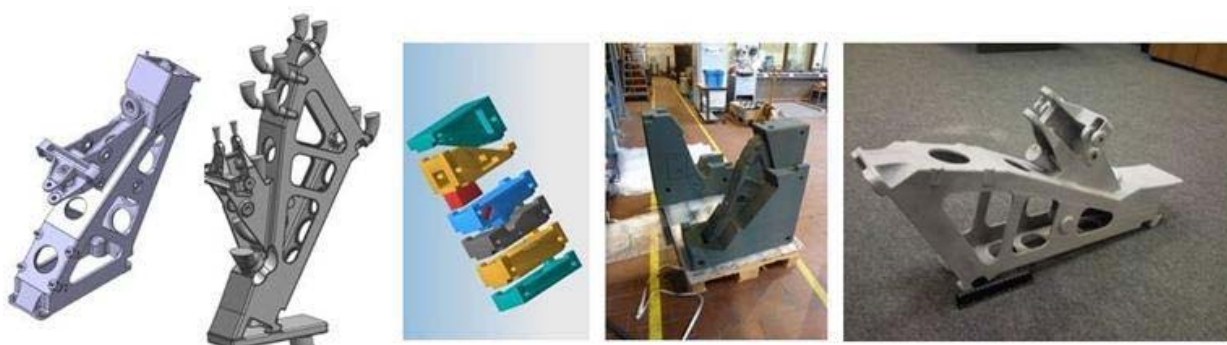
Цикл изготовления отливки детали «постамент» при использовании новых технологий
